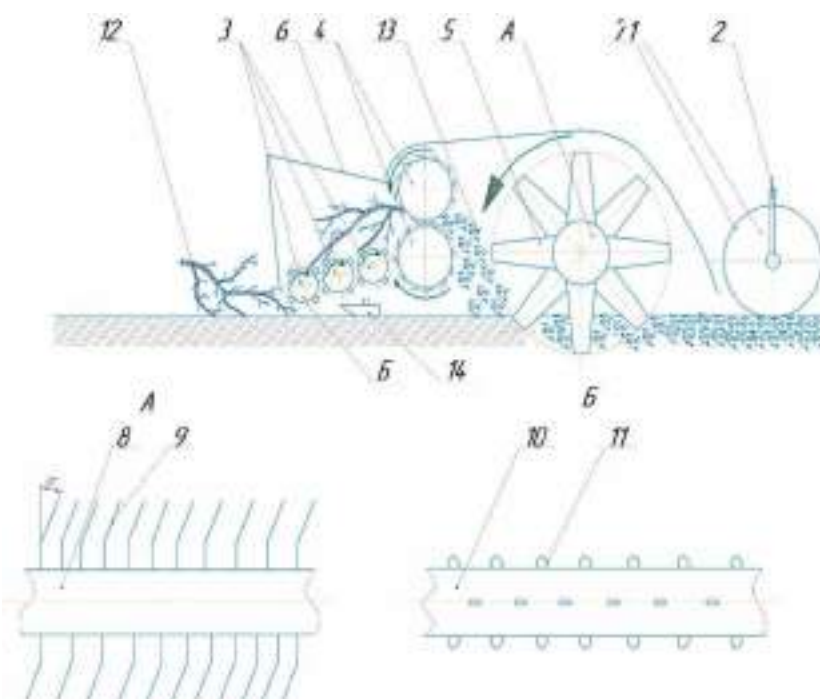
Будова та робота проектної машини: 1 – Опорне колесо; 2 – Регулюючий гвинт глибини обробки ґрунту; 3 – подаючі вальці; 4 – подрібнюючий пристрій; 5 – фреза; 6 – приймальний щиток; 7- відбивний щиток; 8 – вал фрези; 9 – ніж; 10 – вал подаючого вальця; 11 – скребок; 12 – обрізки деревини; 13 – подрібнені обрізки; 14 – копір рельєфу ґрунту.
